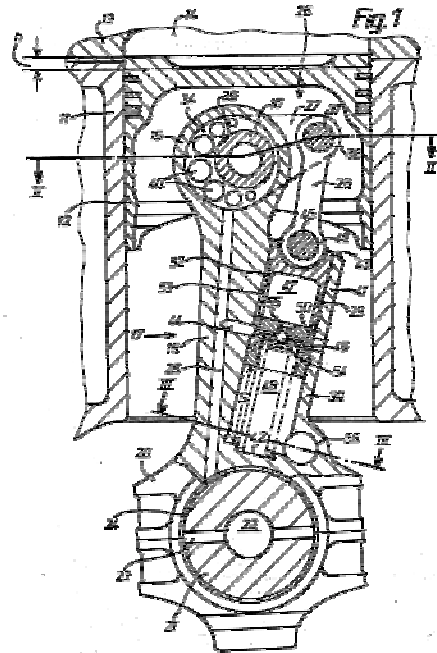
Versuchsmotor mit exzentrischer Kolbenbolzenlagerung [13]
